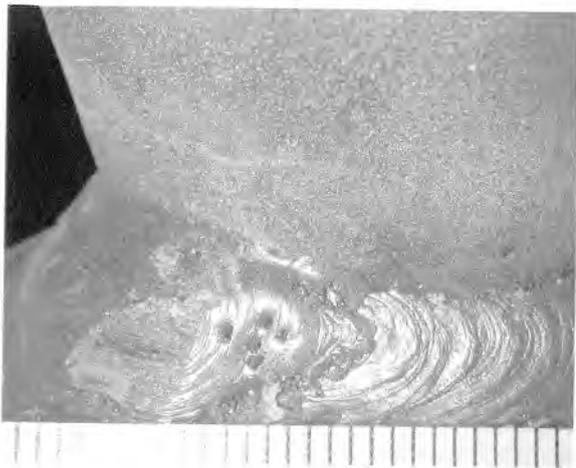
Скопление включений (пяти пор) в угловом сварном соединении штуцера с трубопроводом
